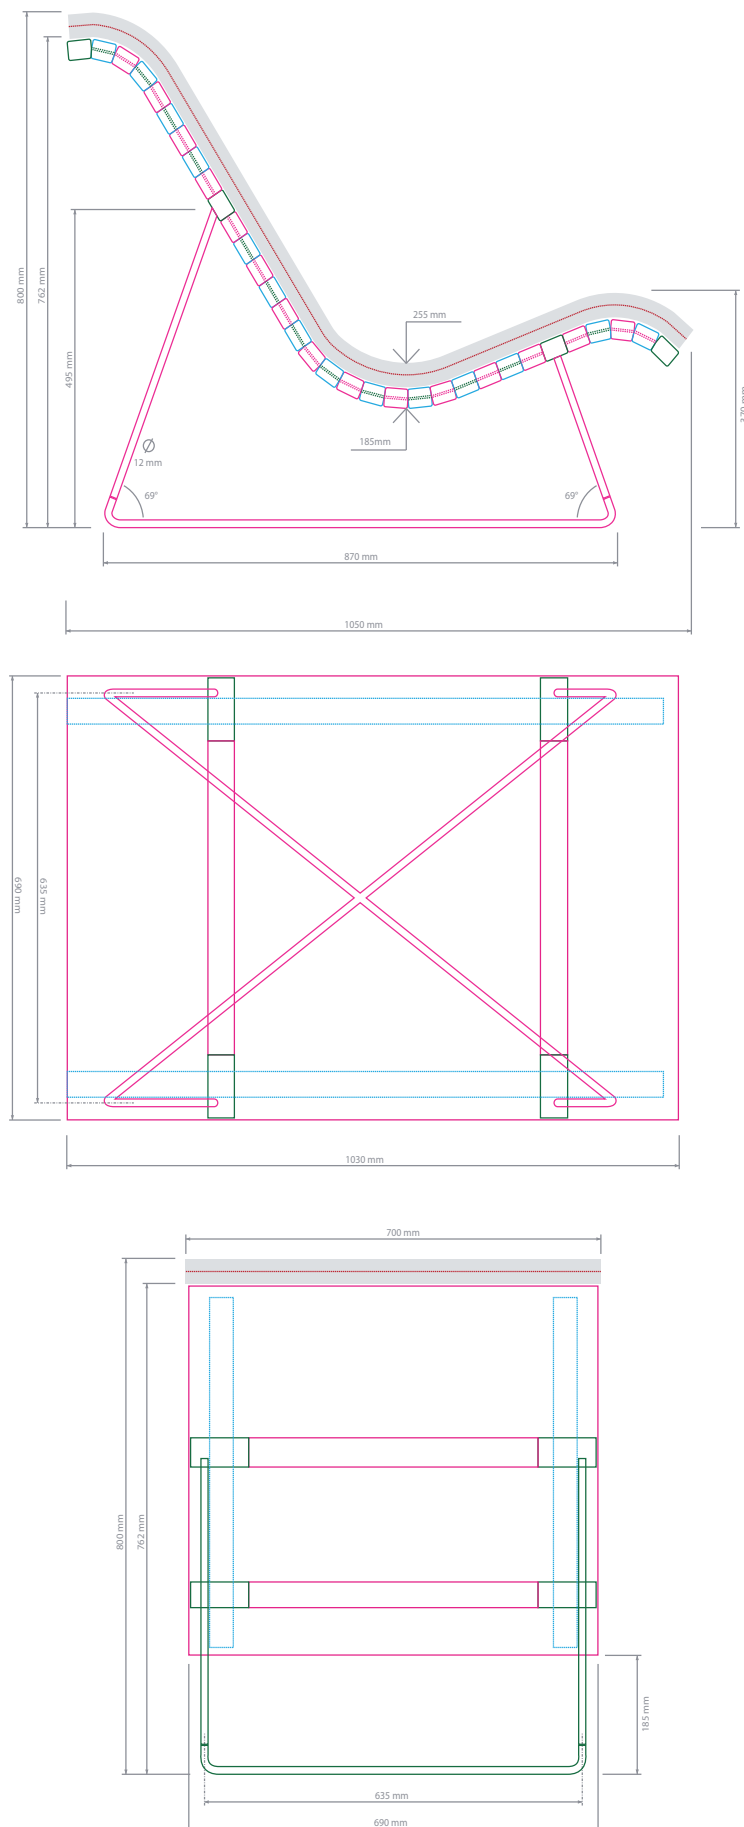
Konstrukční detaily - Propojení nohou způsobem zasunutí trubek do sebe
